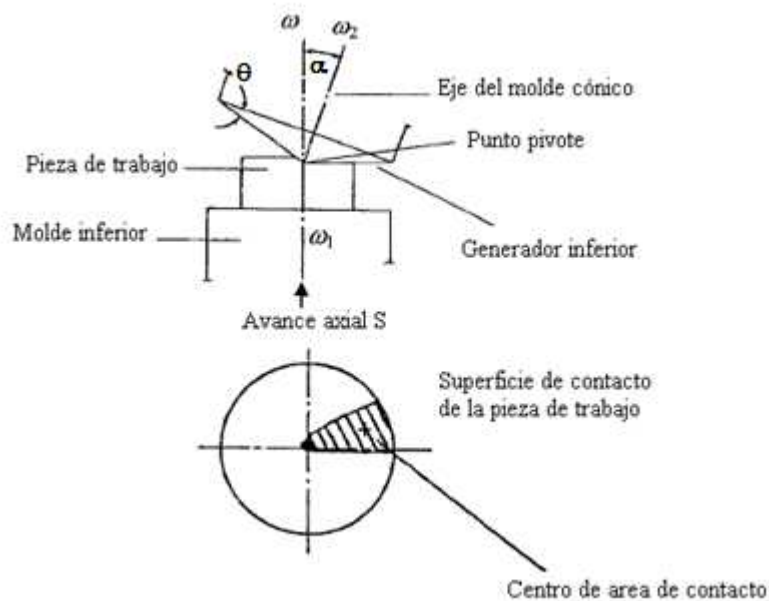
3 Relaciones entre la herramienta inclinada, la pieza de trabajo y la herramienta opuesta (Standring P. M., 2001)
